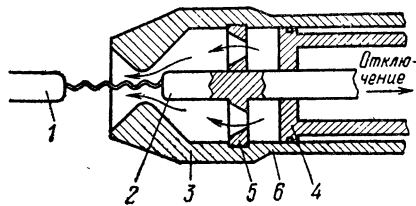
Дугогасительное устройство элегазового выключателя с автопневматическим дутьем.
